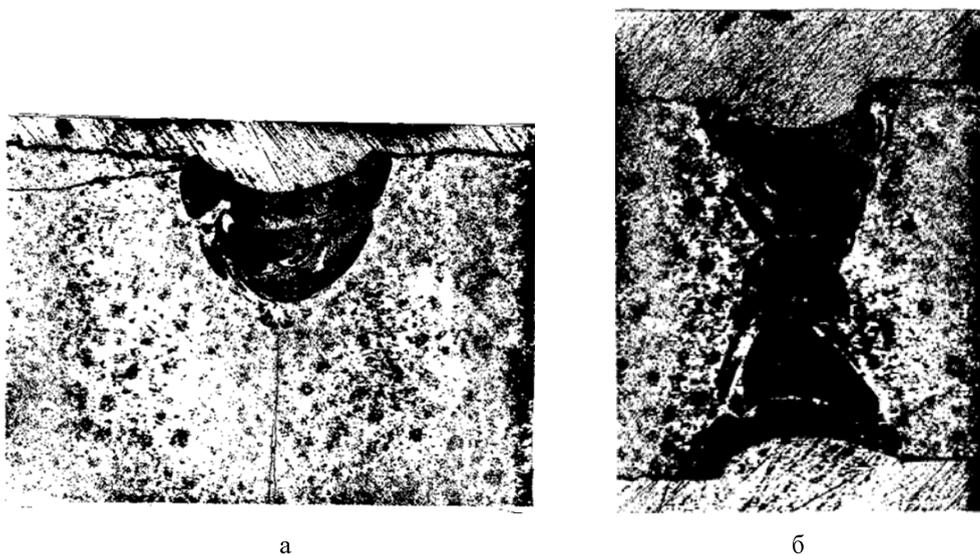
Микроструктура сварного соединения цериевых пластин методом лазерной сварки:
